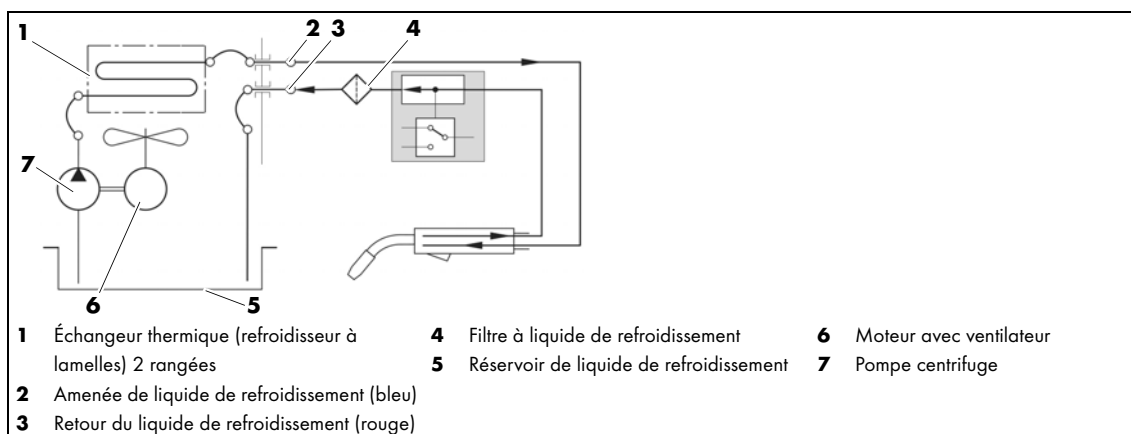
Vue d'ensemble du circuit du liquide de refroidissement
